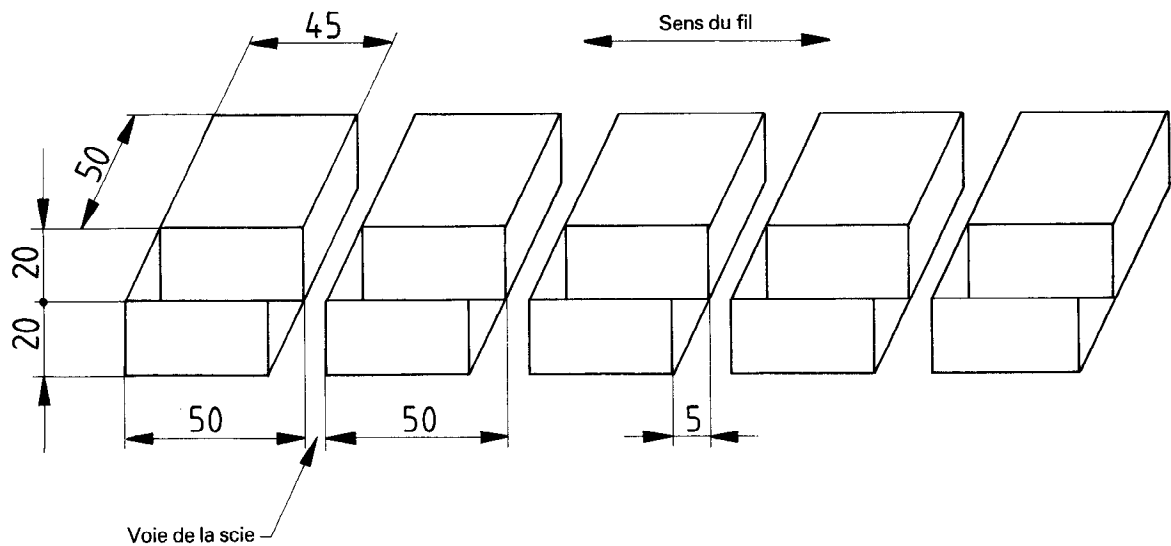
Méthode de découpage des éprouvettes dans les assemblages
